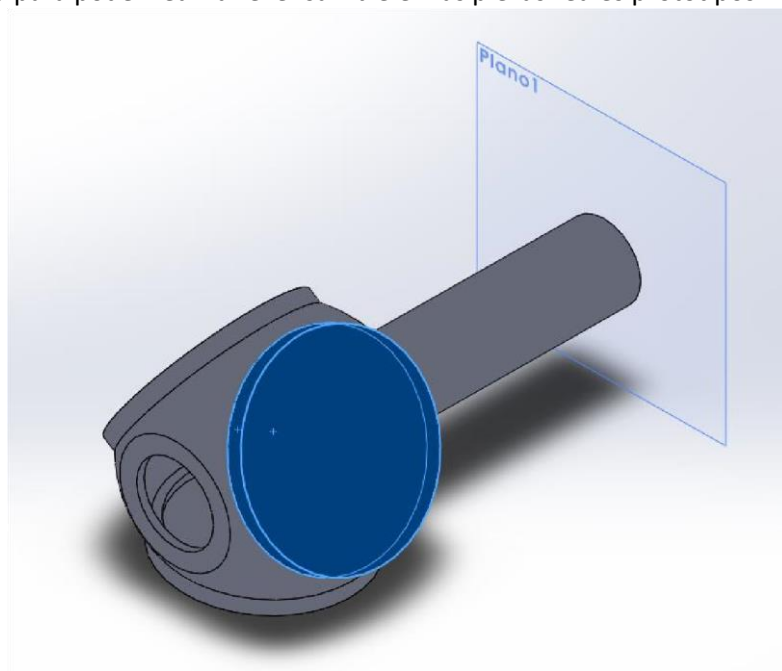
Capas cilíndricas para facilitar el ensamblaje.
